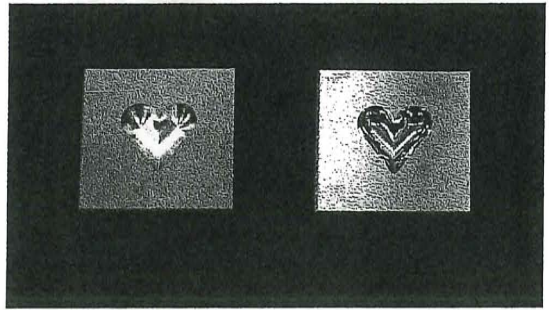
切削加工後(左)と切削加工後、磨き加工後(右)
